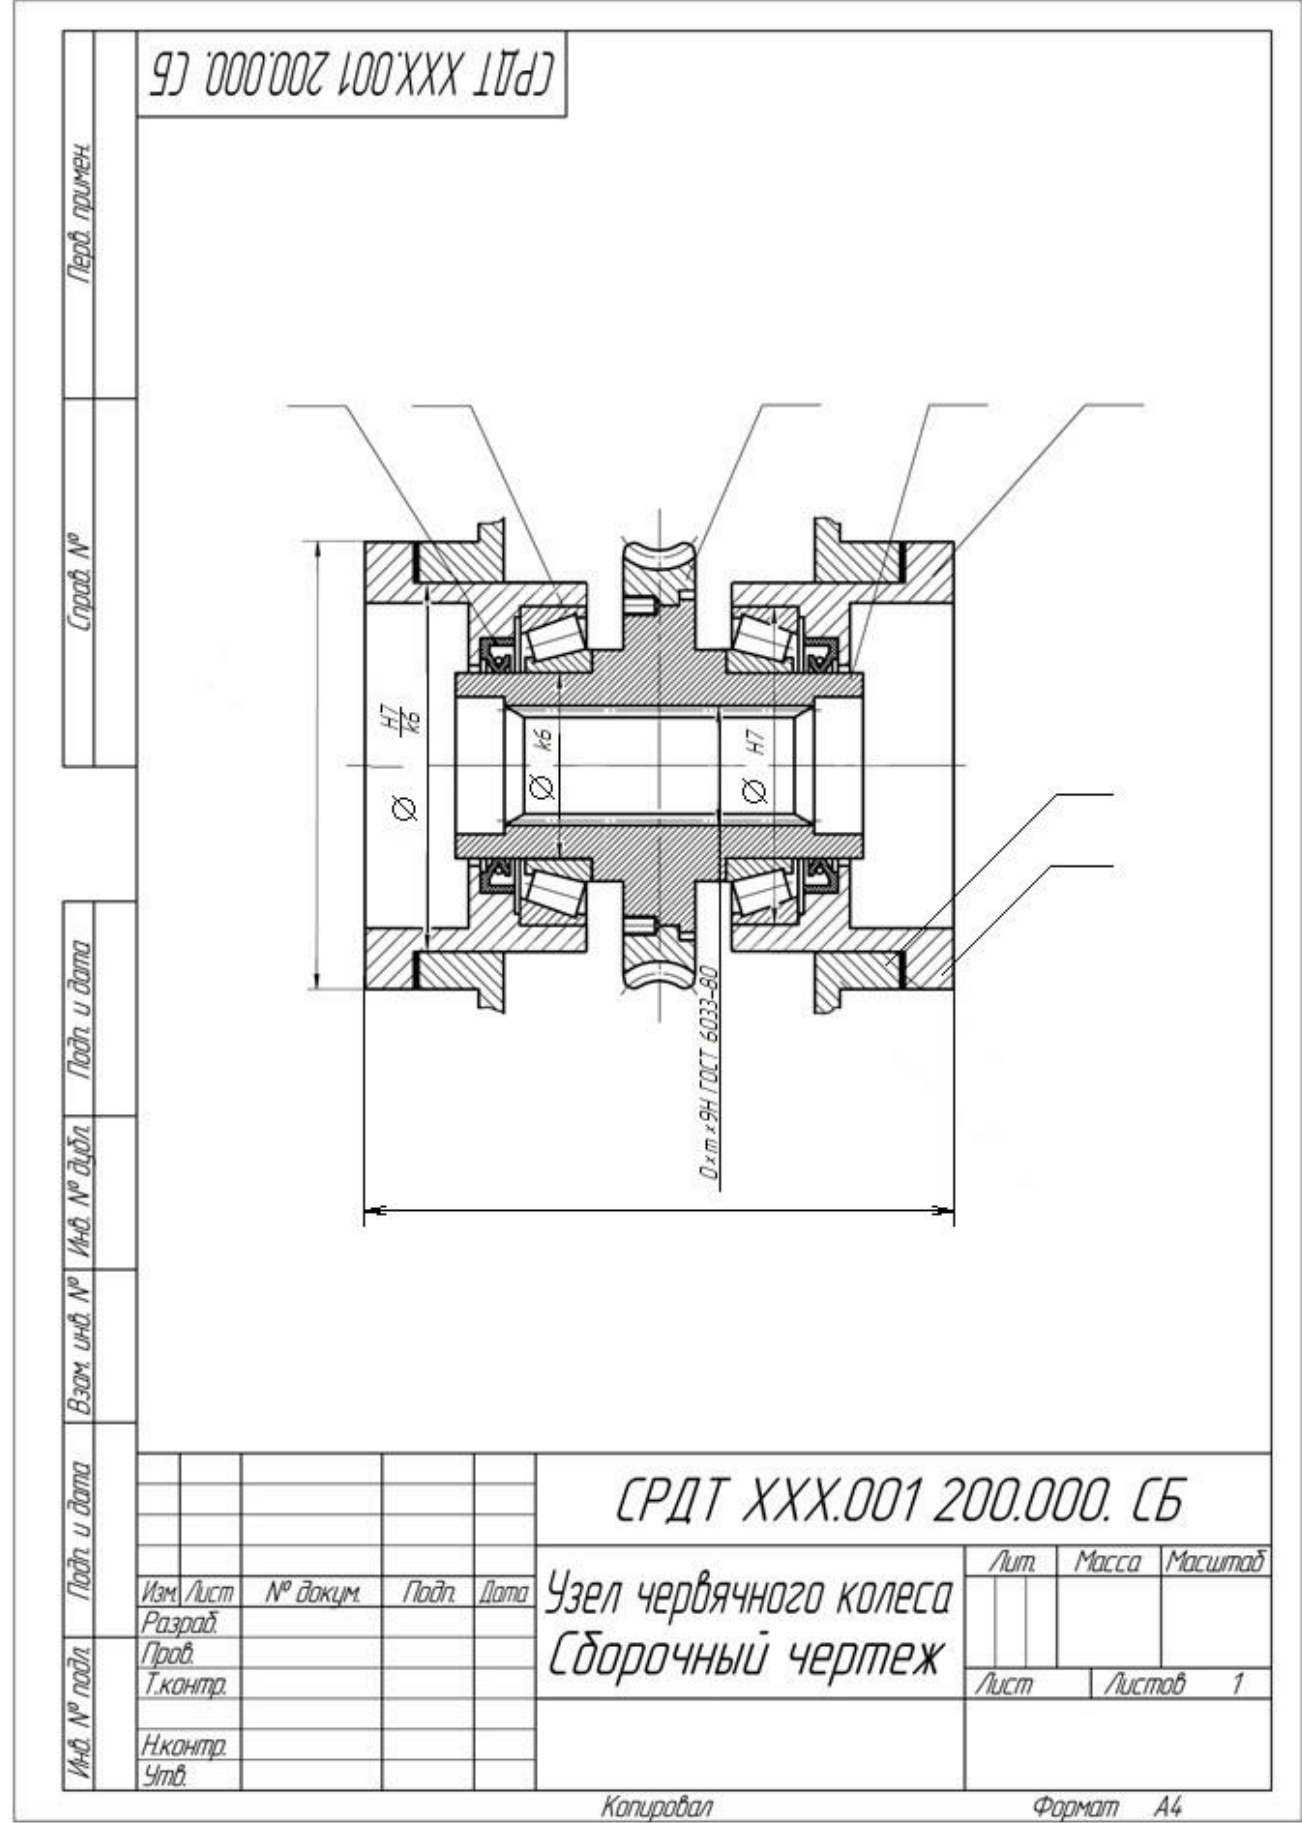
В.6 – Сборочный чертеж узла вала колеса червячного
